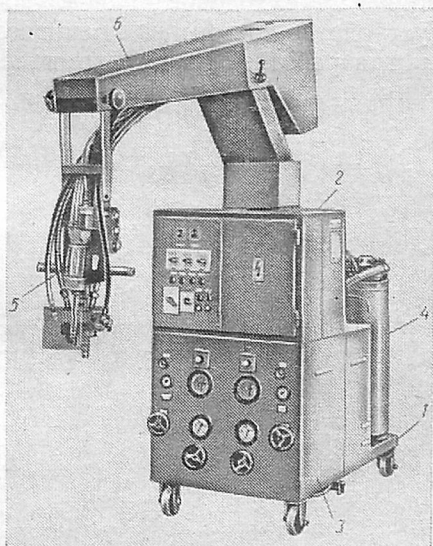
Передвижная установка для формирования изделий из полиуретана
